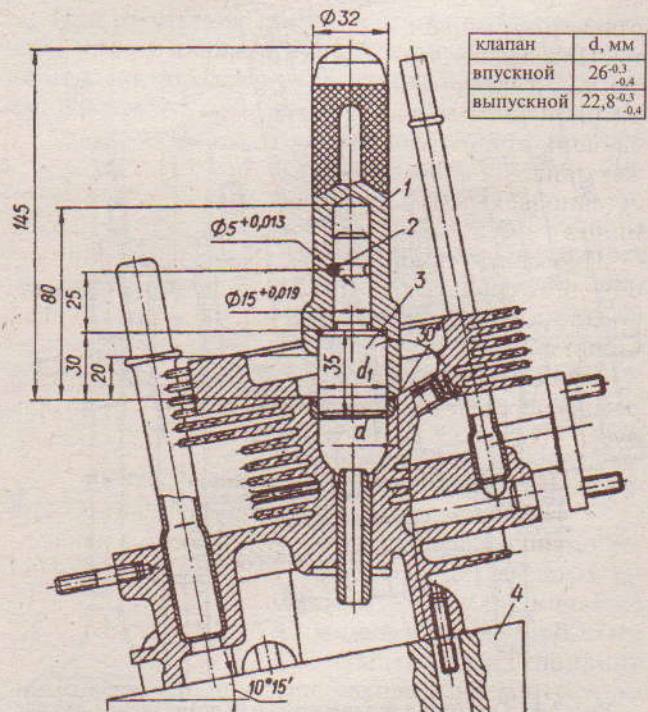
Оправка для зачеканки седла клапана: 1 - оправка; 2 - штифт; 3 - вставка; 4 - подставка
